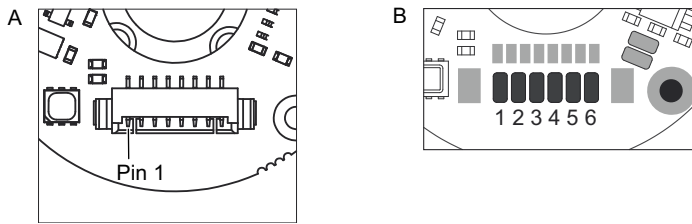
Pinbelegung RLS Encoder – AksIM-2 – Ansicht von oben
